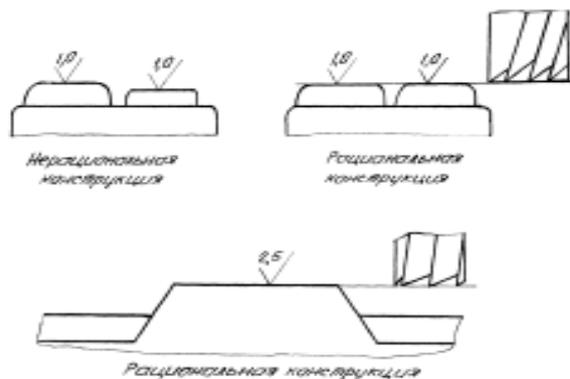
Примеры различного расположения обрабатываемых поверхностей
